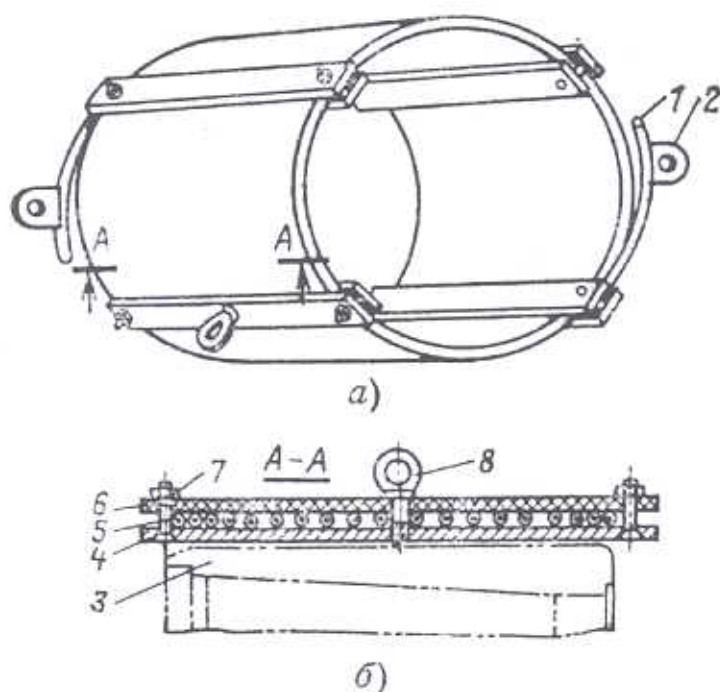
Жесткий индуктор для нагрева бандажей:
